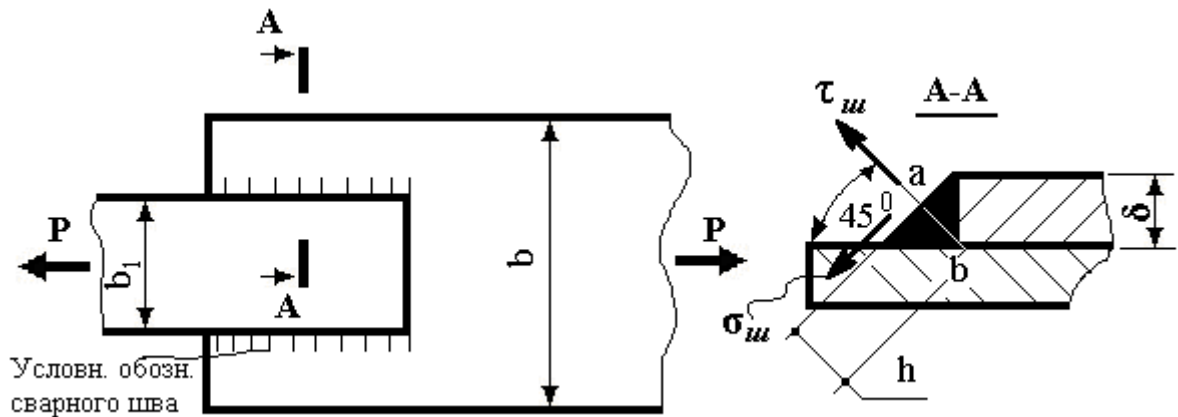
Сварные соединения фланговыми швами
